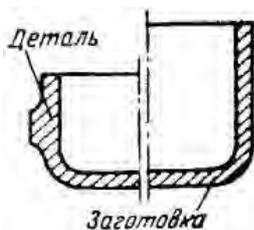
Высадка наружного утолщения на полой заготовке
